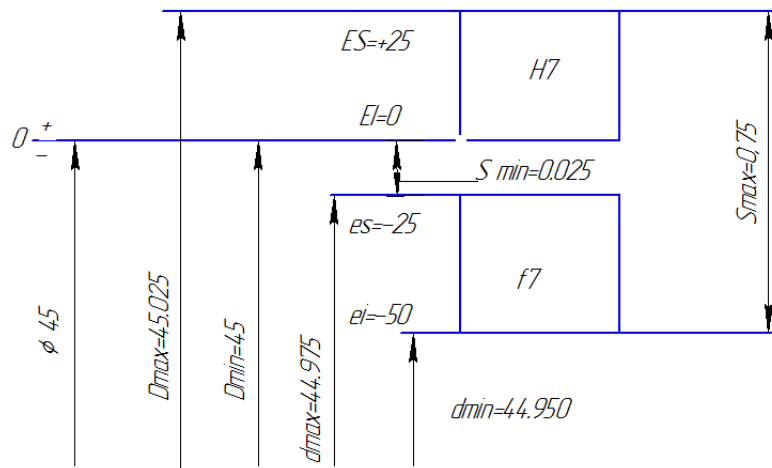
Схема розташування полів допусків деталей з'єднання  $\varnothing 45 \frac{H7}{f7}$
